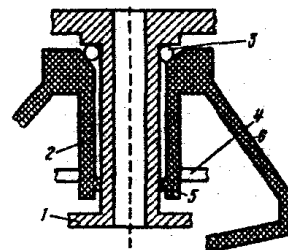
Цилиндрическая ось полукинематического типа с шариковой опорой в теодолитах типа ОТ-02: 1-ось алидады; 2-втулка алидады; 3-шарикоподшипники (опора алидады); 4-лимб; 5-ведущий пояс; 6-подставка
